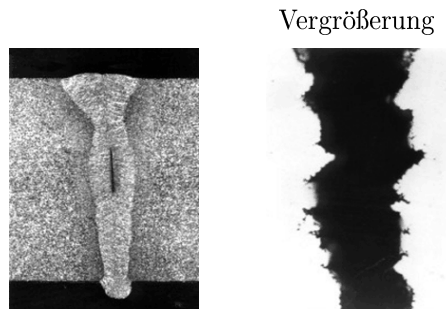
Typischer Heißriß einer Schweißnaht in Aluminium [11].
